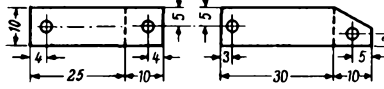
Haltestücke für Seilrollen, Al-Blech, 2 mm. Maßstab 1 : 2
